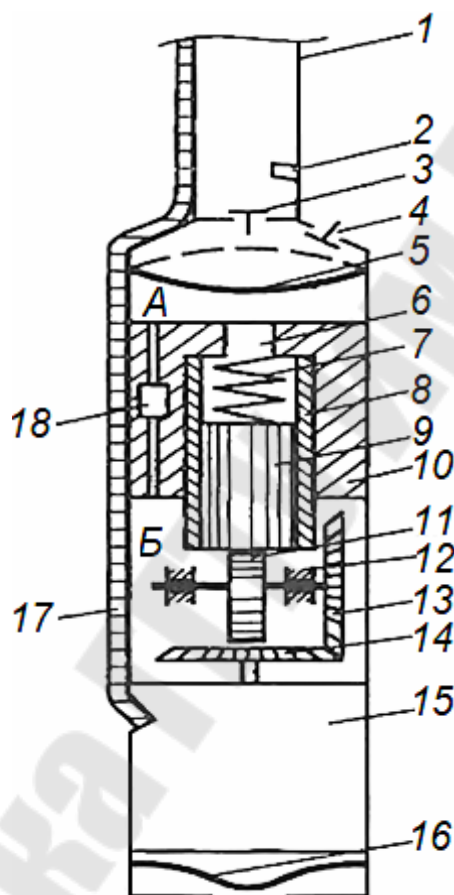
Принципиальная схема погружного агрегата диафрагменной насосной установки: 1 – колонна НКТ; 2 – сливной клапан; 3 – нагнетательный клапан; 4 – всасывающий клапан; 5 – диафрагма; 6 – осевой канал; 7 – винтовая пружина; 8 – цилиндр; 9 – поршень; 10 – корпус; 11 – эксцентрик; 12 – опора; 13, 14 – зубчатые колеса; 15 – погружной электродвигатель; 16 – компенсационная диафрагма; 17 – электрический кабель; 18 – специальный клапанный узел
